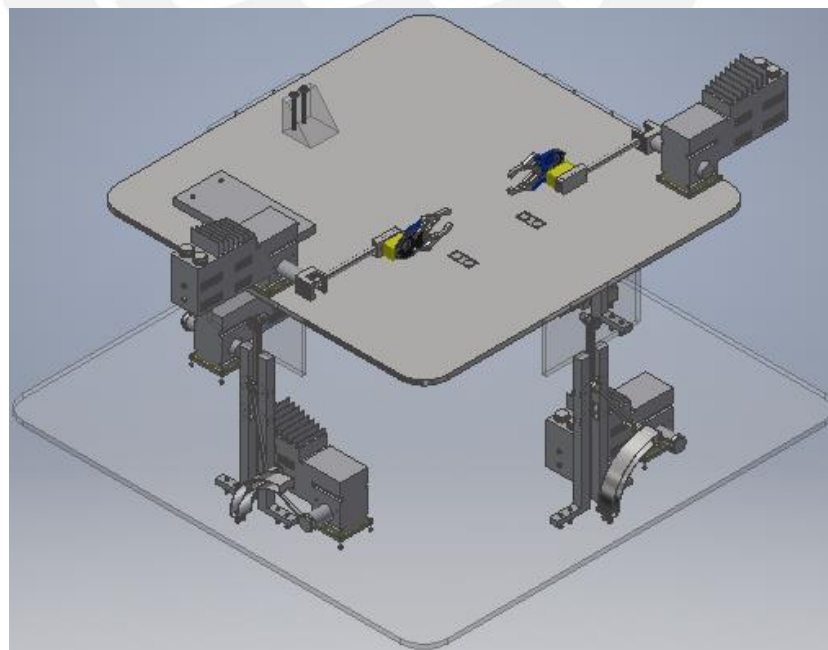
Vista isométrica de la plataforma automática. Fuente: Elaboración propia
